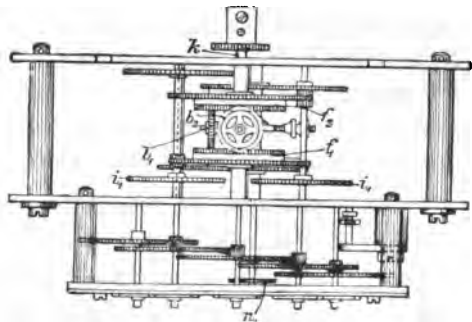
Neuester Aron-Zähler. Grundriss.
